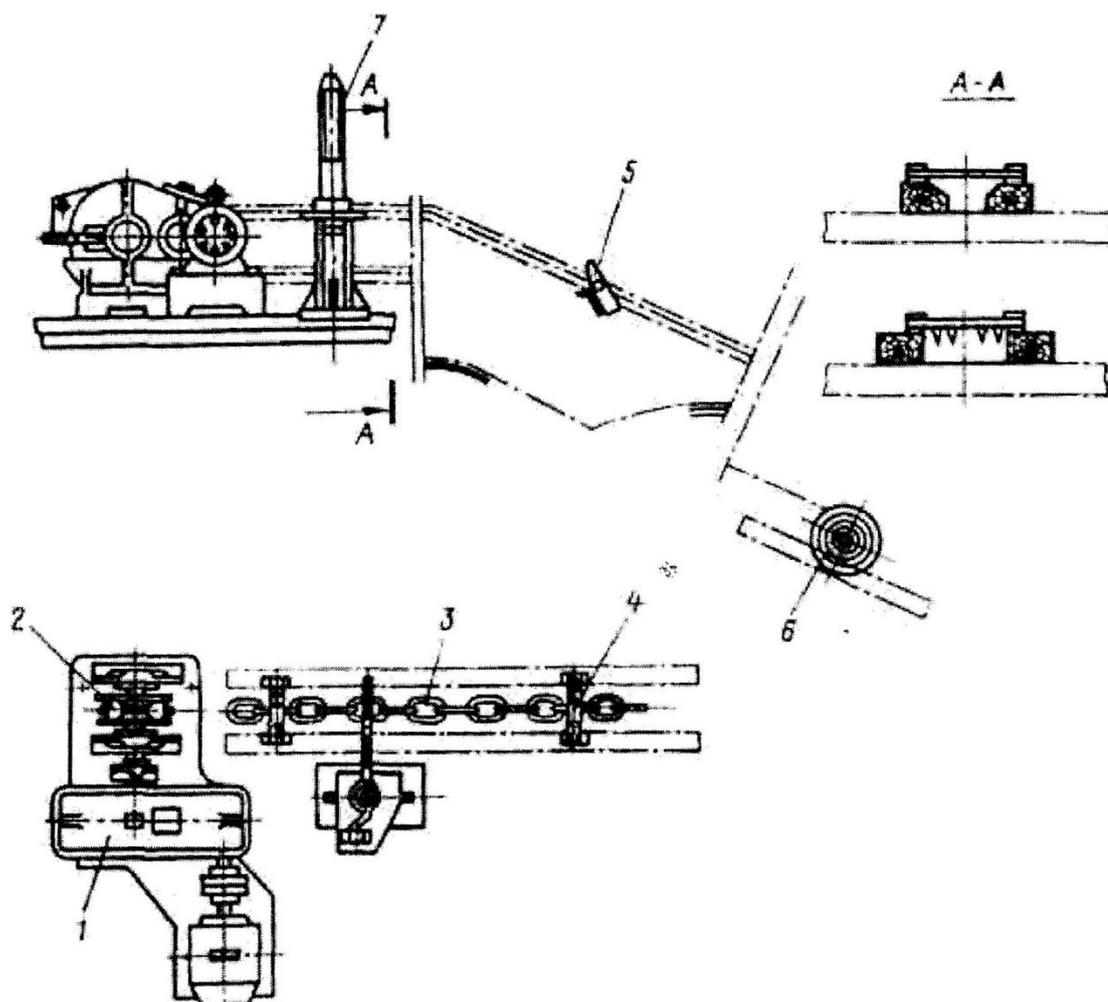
Бревнотаска БА-3: 1 – приводная станция; 2 – приводная звездочка; 3 – тяговая цепь; 4 – поперечина (траверса); 5 – аварийный останов; 6 – холостая звездочка; 7 – автоматический останов
